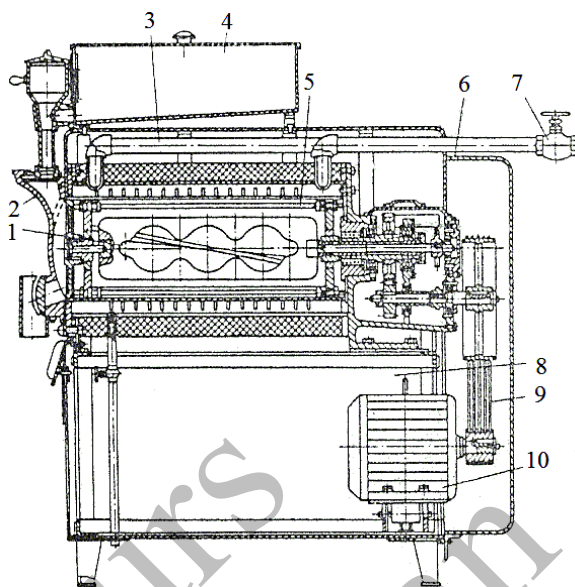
Freezer discontinuu model OFI: 1- agitator; 2- capac; 3- conductă saramură; 4- canea; 5- cilindru de lucru; 6- apărătoare; 7- ventil; 8- postament; 9- curele trapezoidale; 10- electromotor
